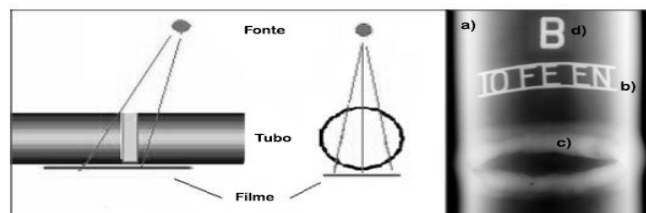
Radiografia PDVD: (a) Parede do tubo; (b) Indicador de qualidade da imagem (IQI); (c) Cordão de solda; (d) marcador indicando o ângulo de exposição da junta soldada. Fonte: adaptada de [8].
